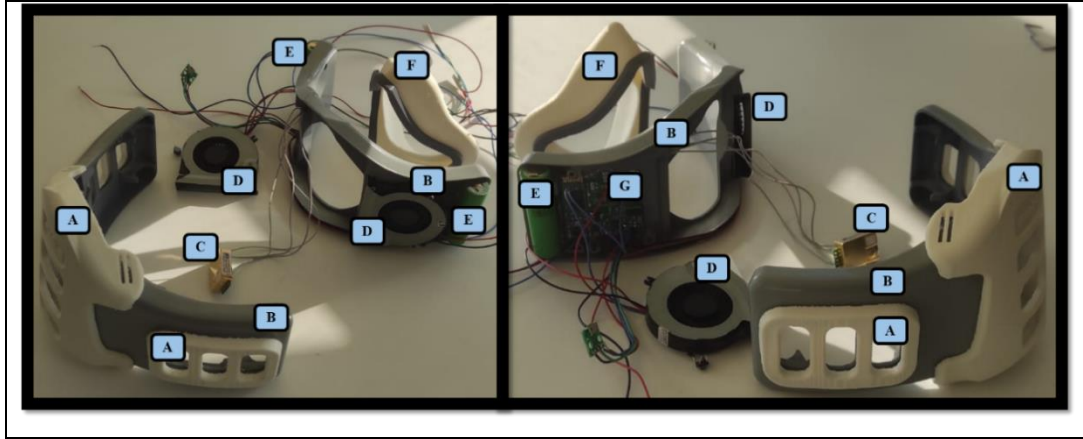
Üretimi tamamlanan PCB kartının maske içerisindeki montajlı hali.
